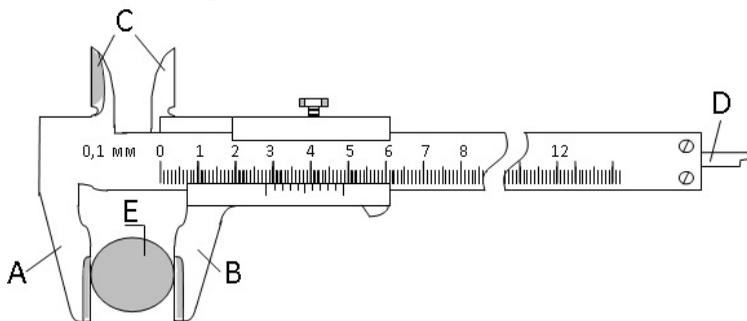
Измерение штангенциркулем диаметра цилиндра.
